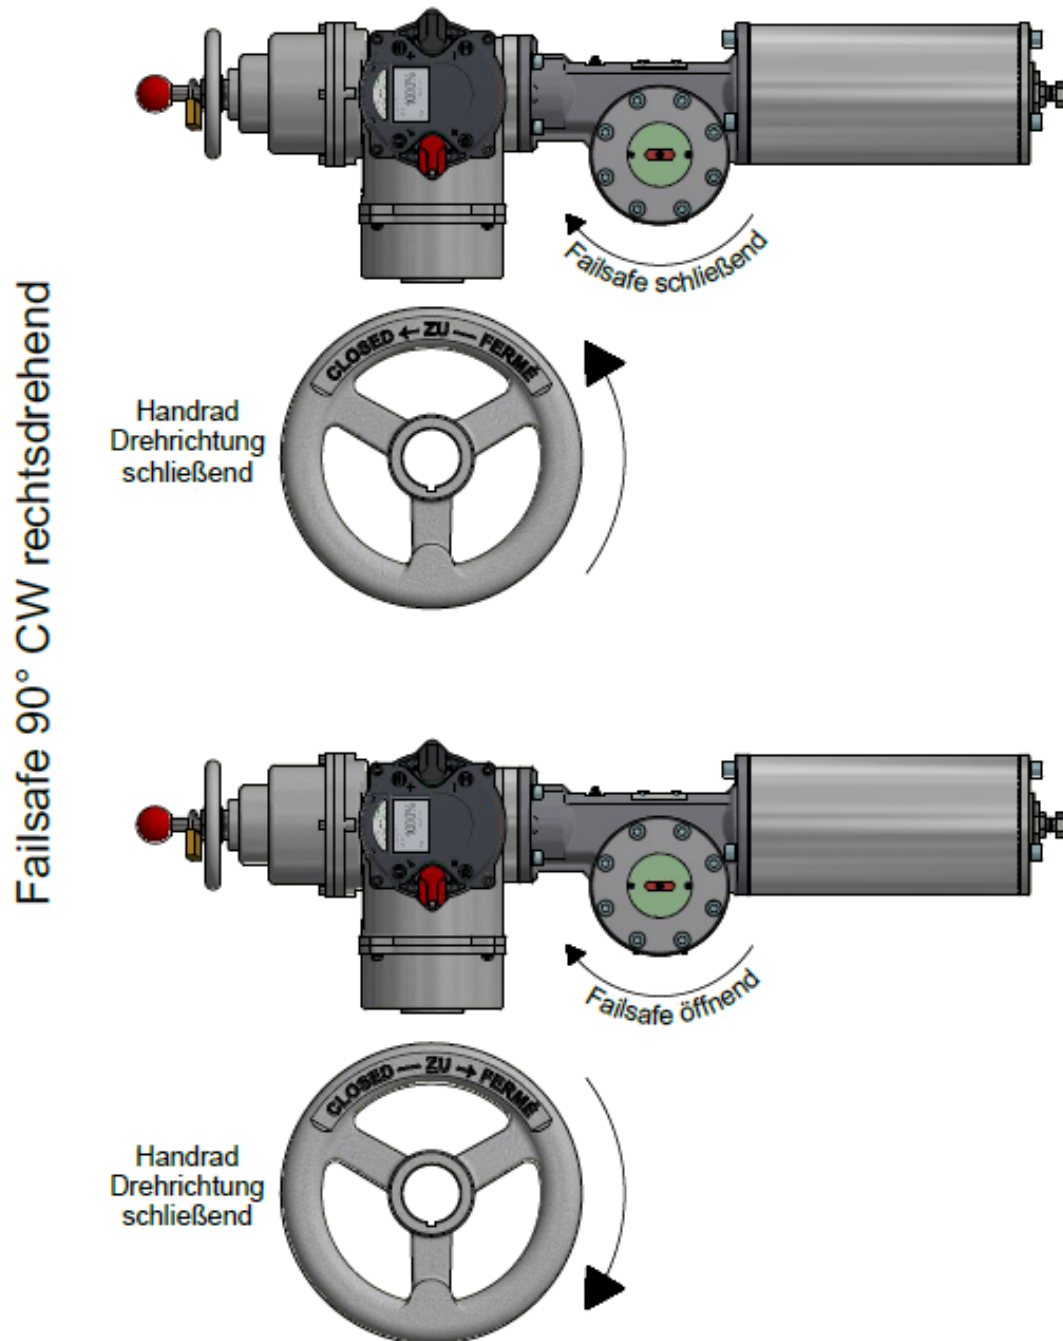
Drehrichtung des Handrades für Failsafe „CW“.
